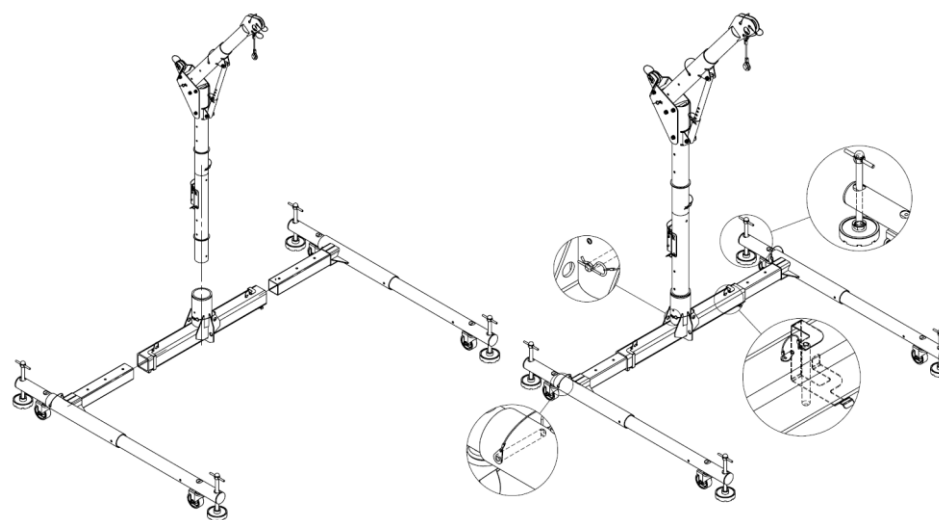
Монтаж СОБ Кран Е11-1Н
